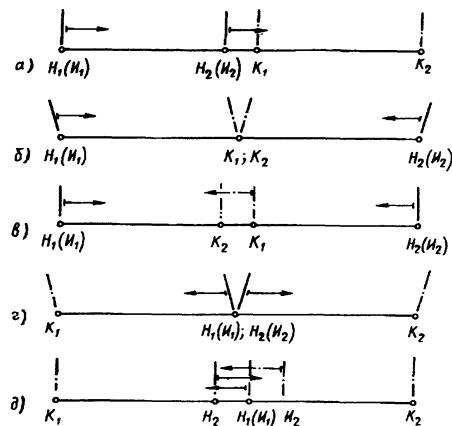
Схемы одновременной сварки участка шва двумя соседними головками, движущимися:
